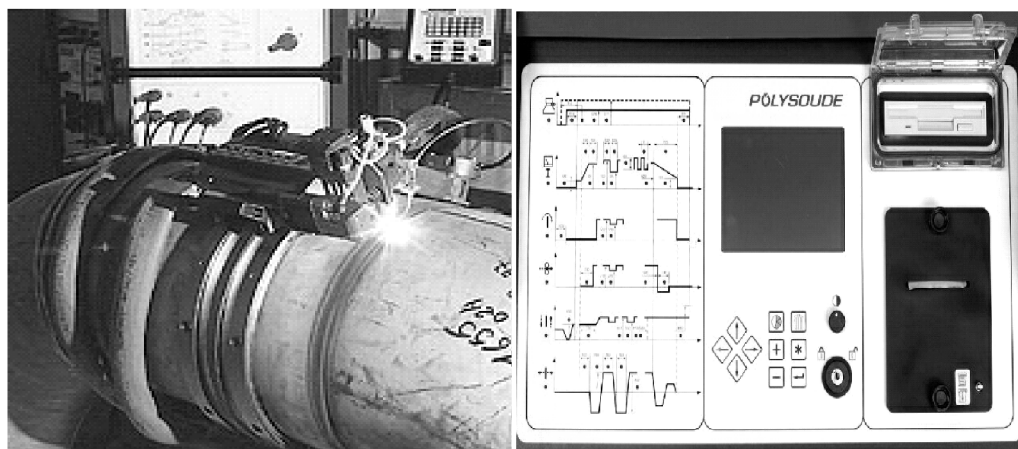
TIG 填丝焊工艺全位置焊管 (POLYSOUDE)
